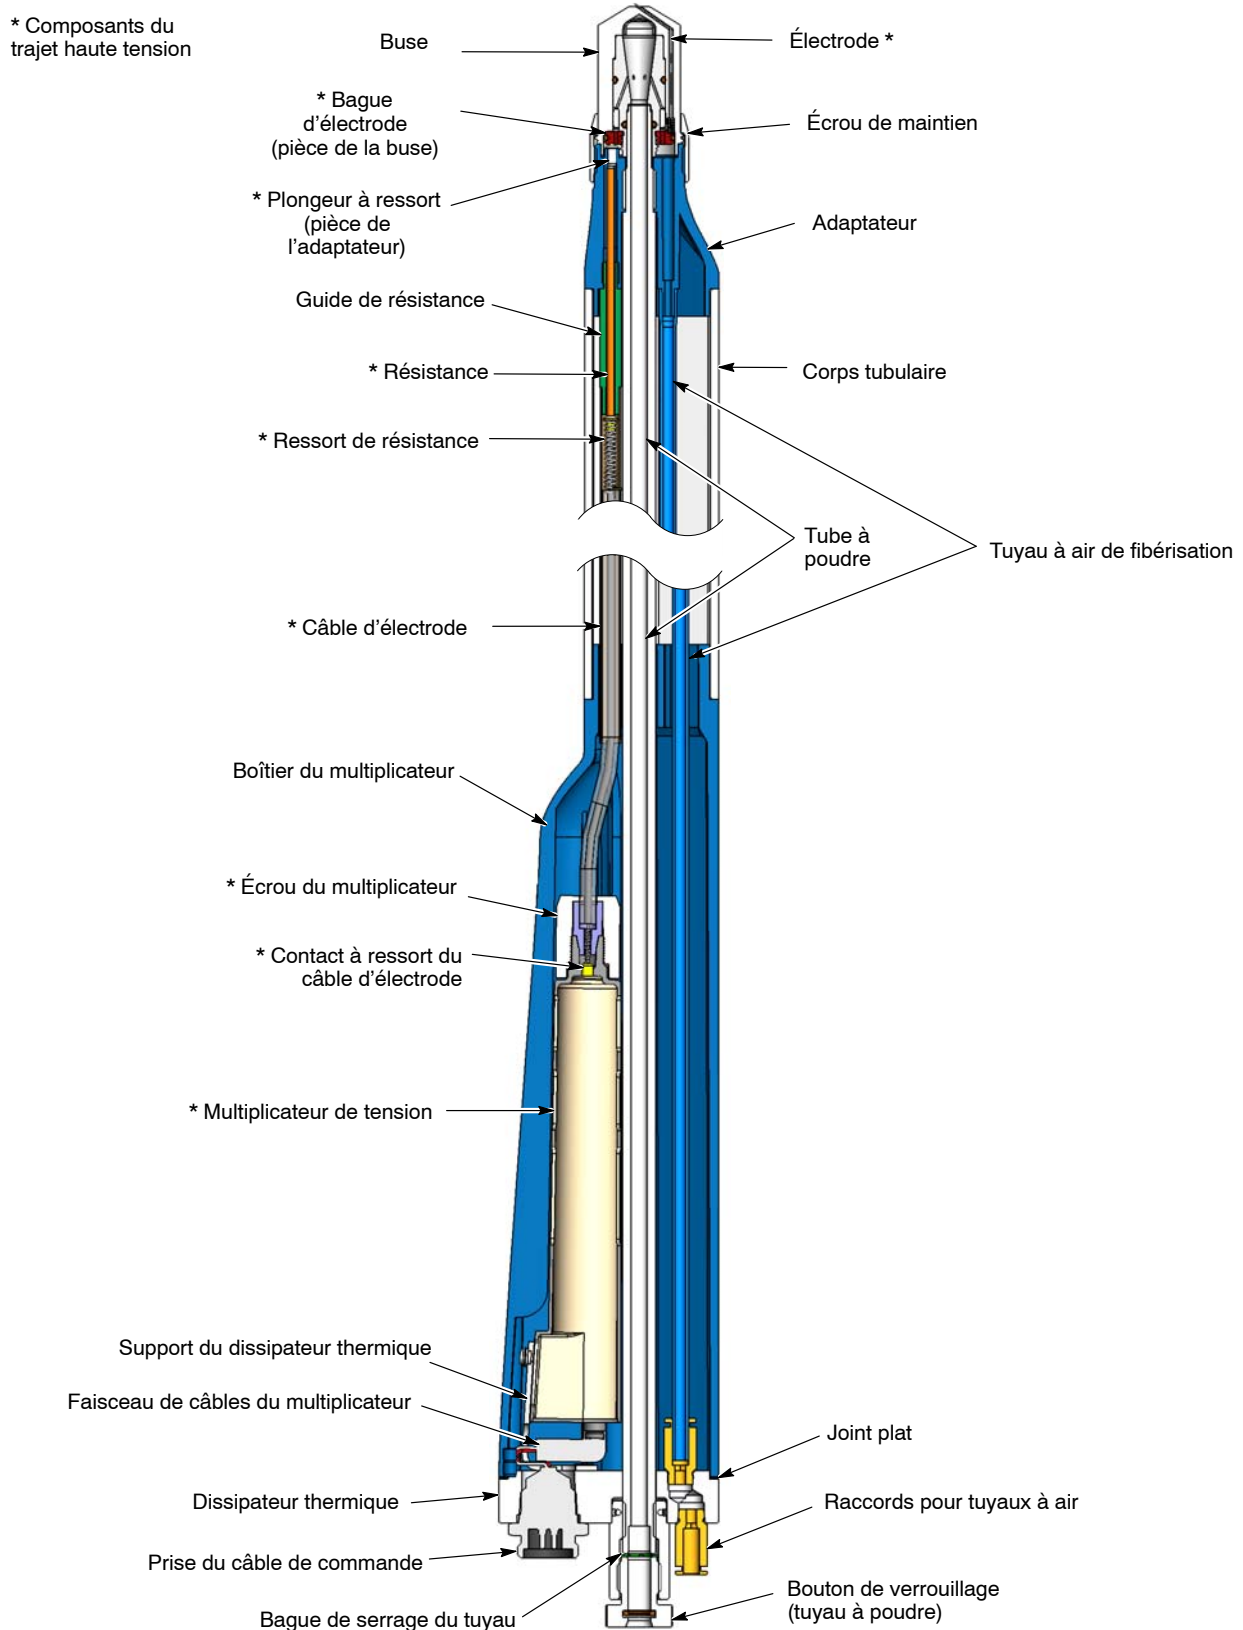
Vue en coupe – Composants et assemblage du pistolet à fixation sur tube
